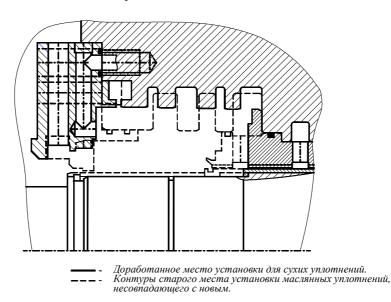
Доработка деталей компрессора при стандартном решении
